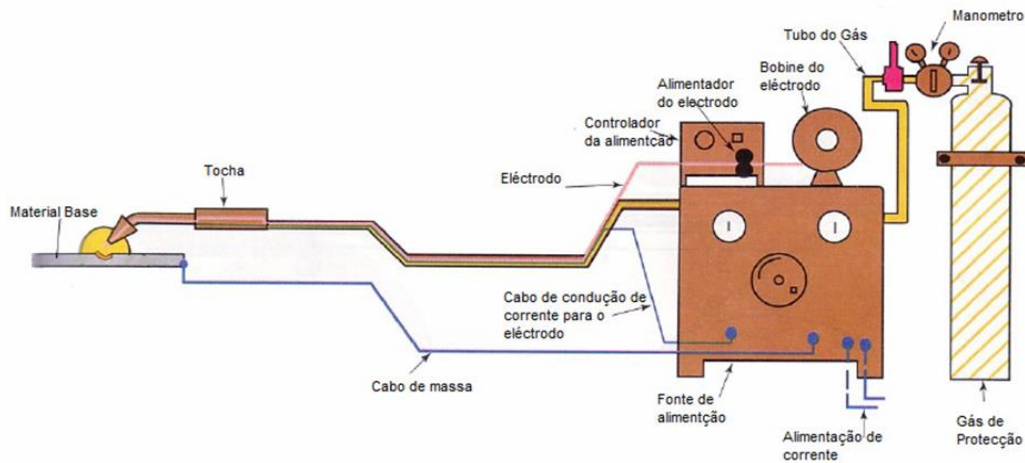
Esquema do equipamento básico para o processo de soldadura MAG [26].
